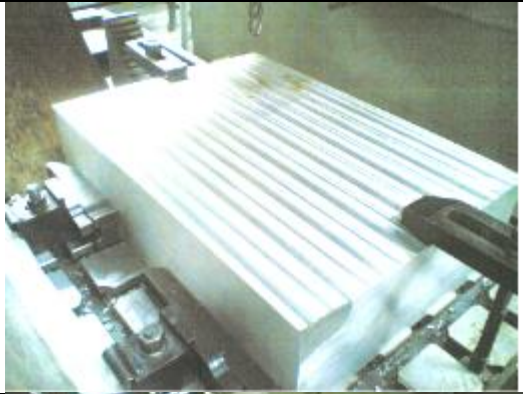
УСП для кріплення заготовки у процесі формоутворення
